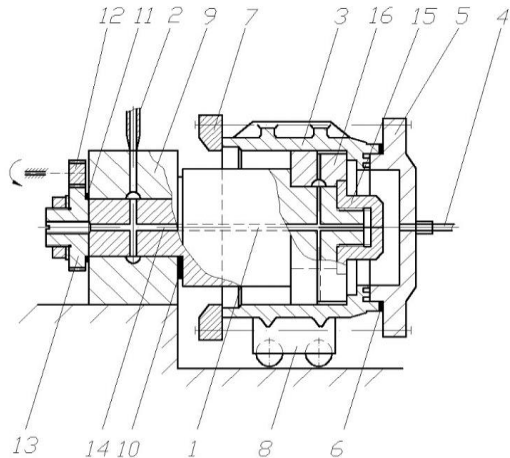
Устройство для нанесения полимерного покрытия на внутреннюю поверхность корпуса роликовой колёсной пары
